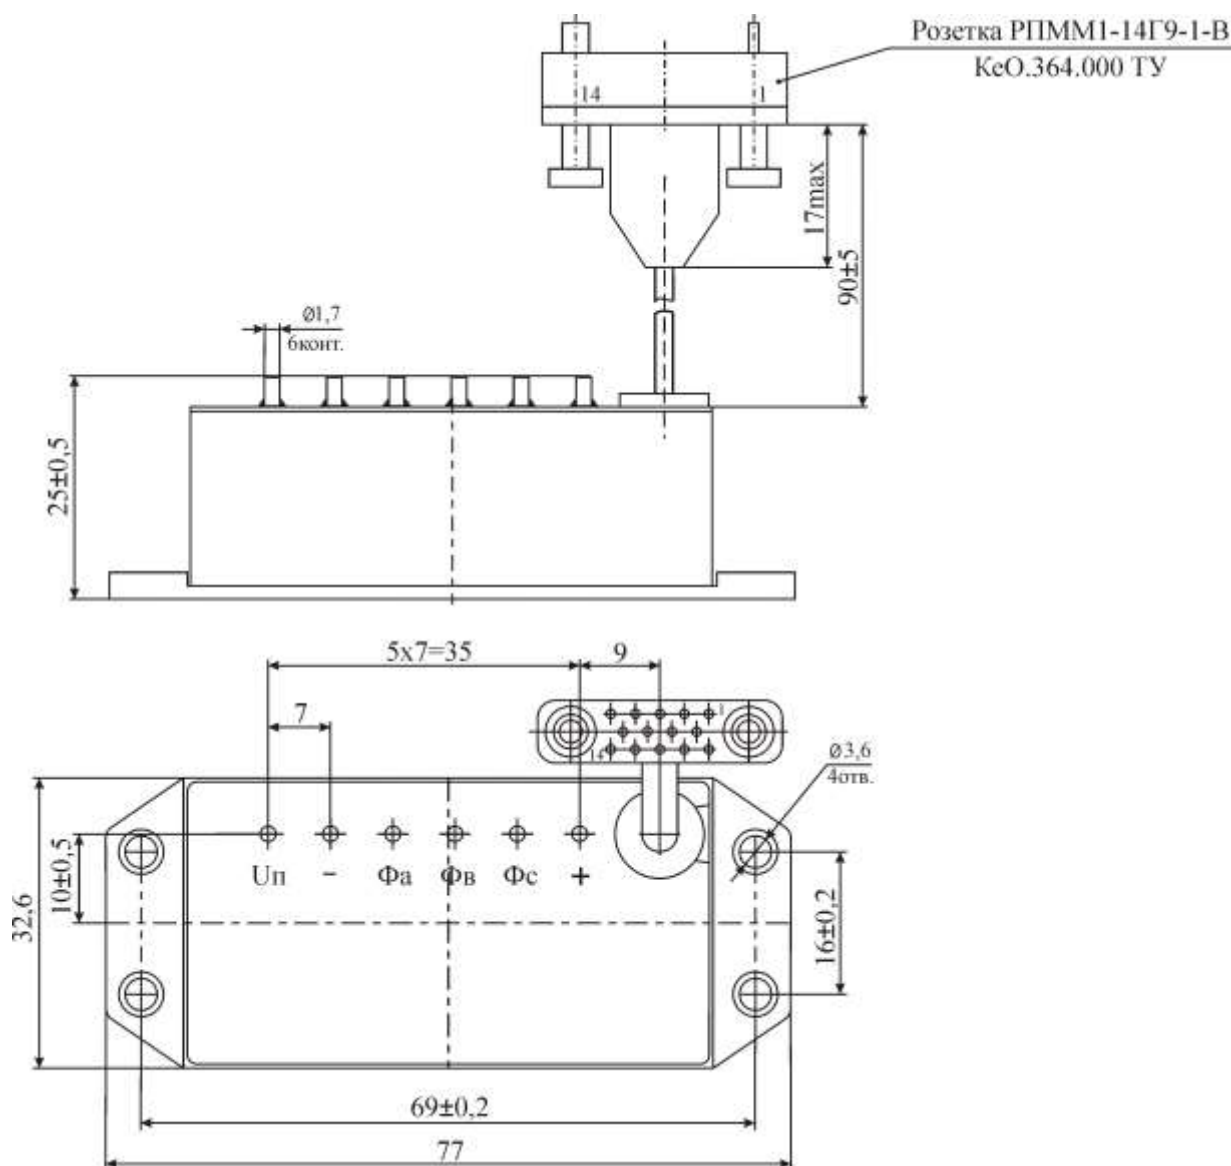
Габаритные и присоединительные размеры 1УМ14А
